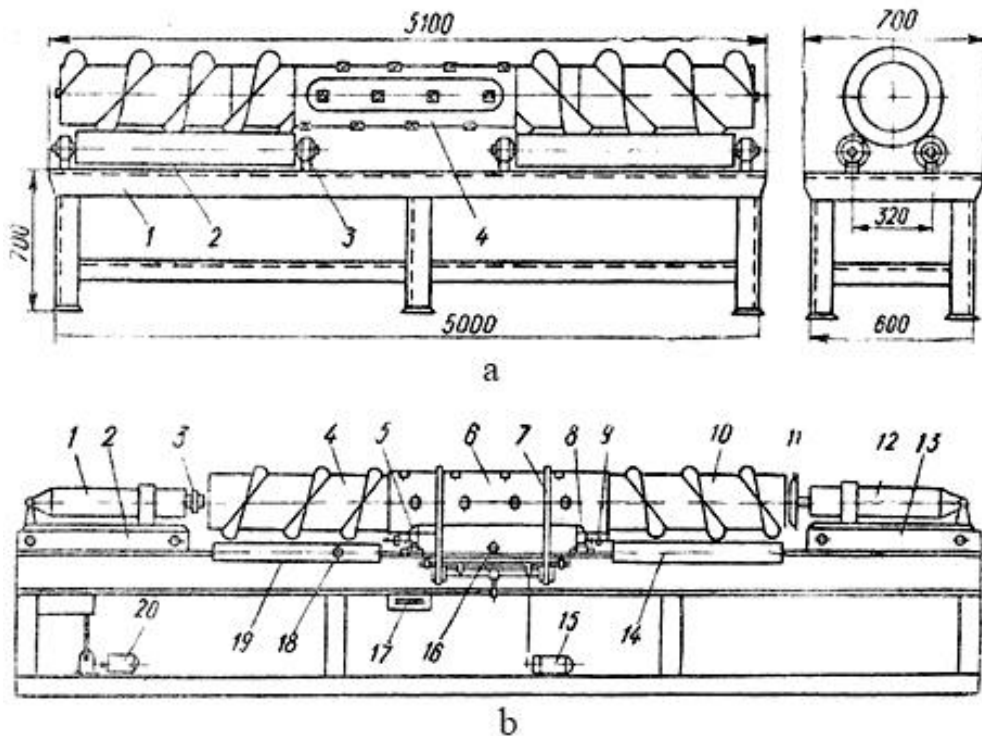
Обладнання для відновлення шнеків жниварок зернозбиральних комбайнів: а – обертач шнека жниварки: 1 – рама; 2 – валець; 3 – підшипник; 4 – шнек жниварки; б – схема станда для заpresування крайніх труб шнеків жниварок зернозбиральних комбайнів: 1, 12 – гідроциліндри; 2, 13 – напрямні; 3 – пуансон; 4, 10 – крайні труби шнека; 5, 8 – фіксатори; 6 – центральна труба шнека; 7 – пас, 9 – коток; 11 – диск; 14, 19 – вальці; 15, 20 – електродвигуни; 16, 18 – місця кріплення фіксаторів; 17 – пульт керування
